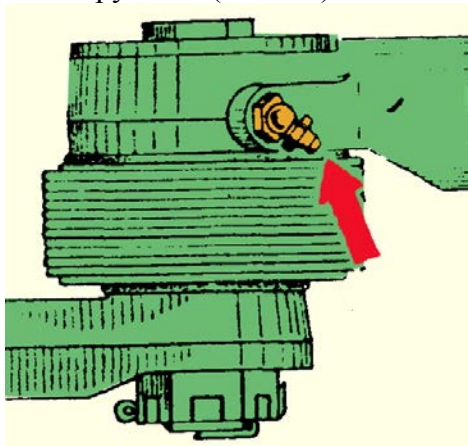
ОК-20 – Смазывание смазкой Литол-24 шарнирных соединений колёсных тяг рулевого привода
